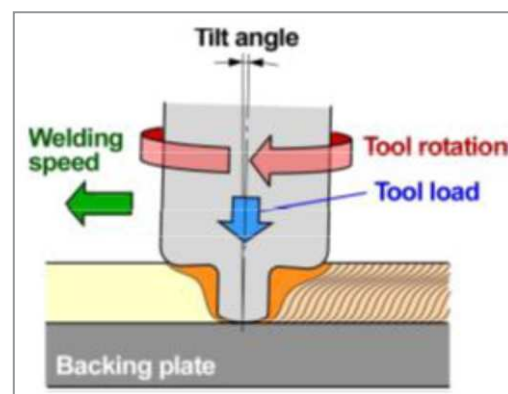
Heat Zone Hasil *Friction Stir Welding* (R. Rai, A, d
